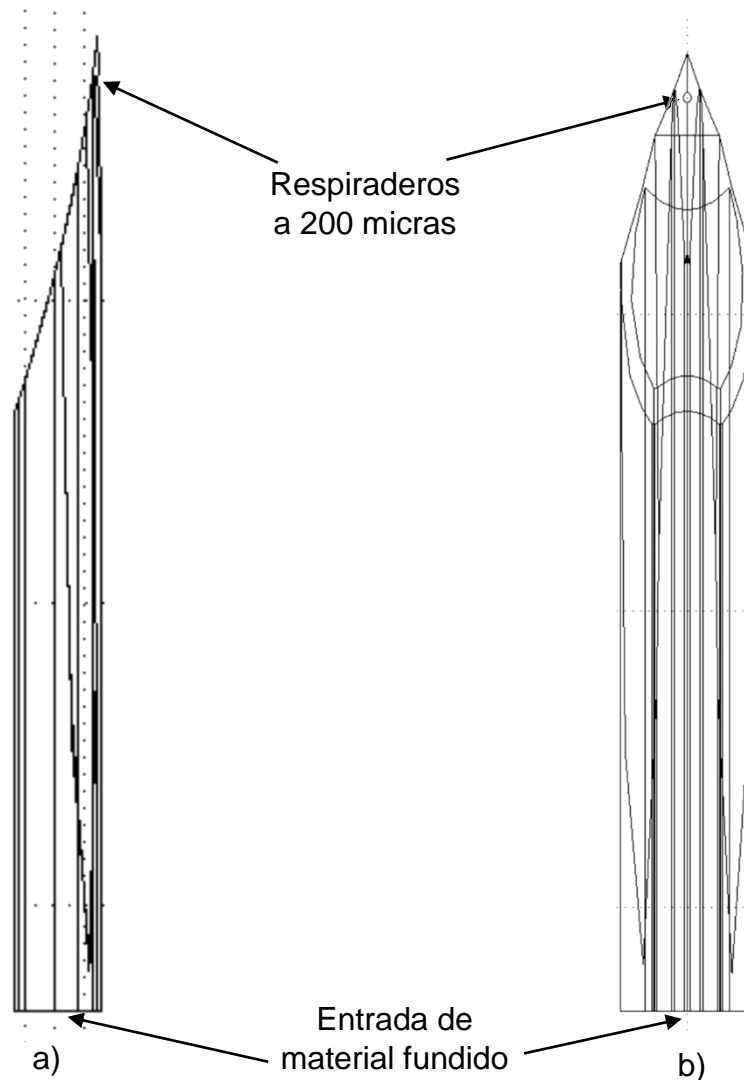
Condiciones de frontera, a) vista lateral del molde y b) vista superior del molde.
